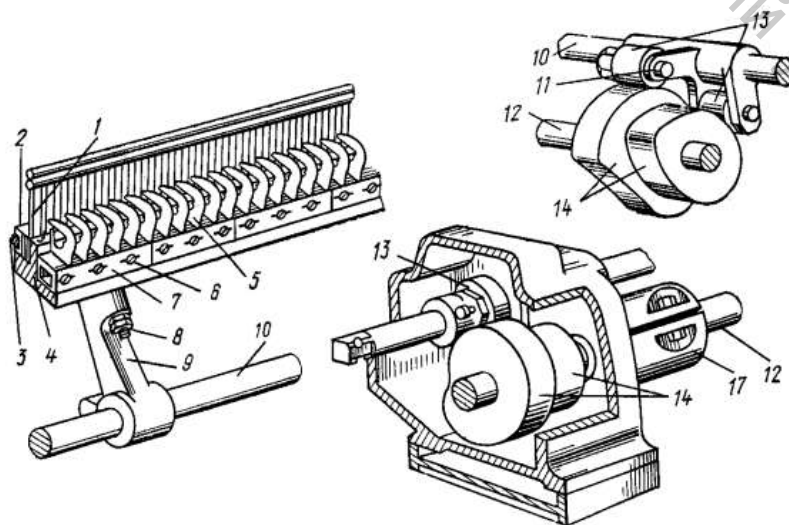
Батанный механизм ткацкого станка СТБ
